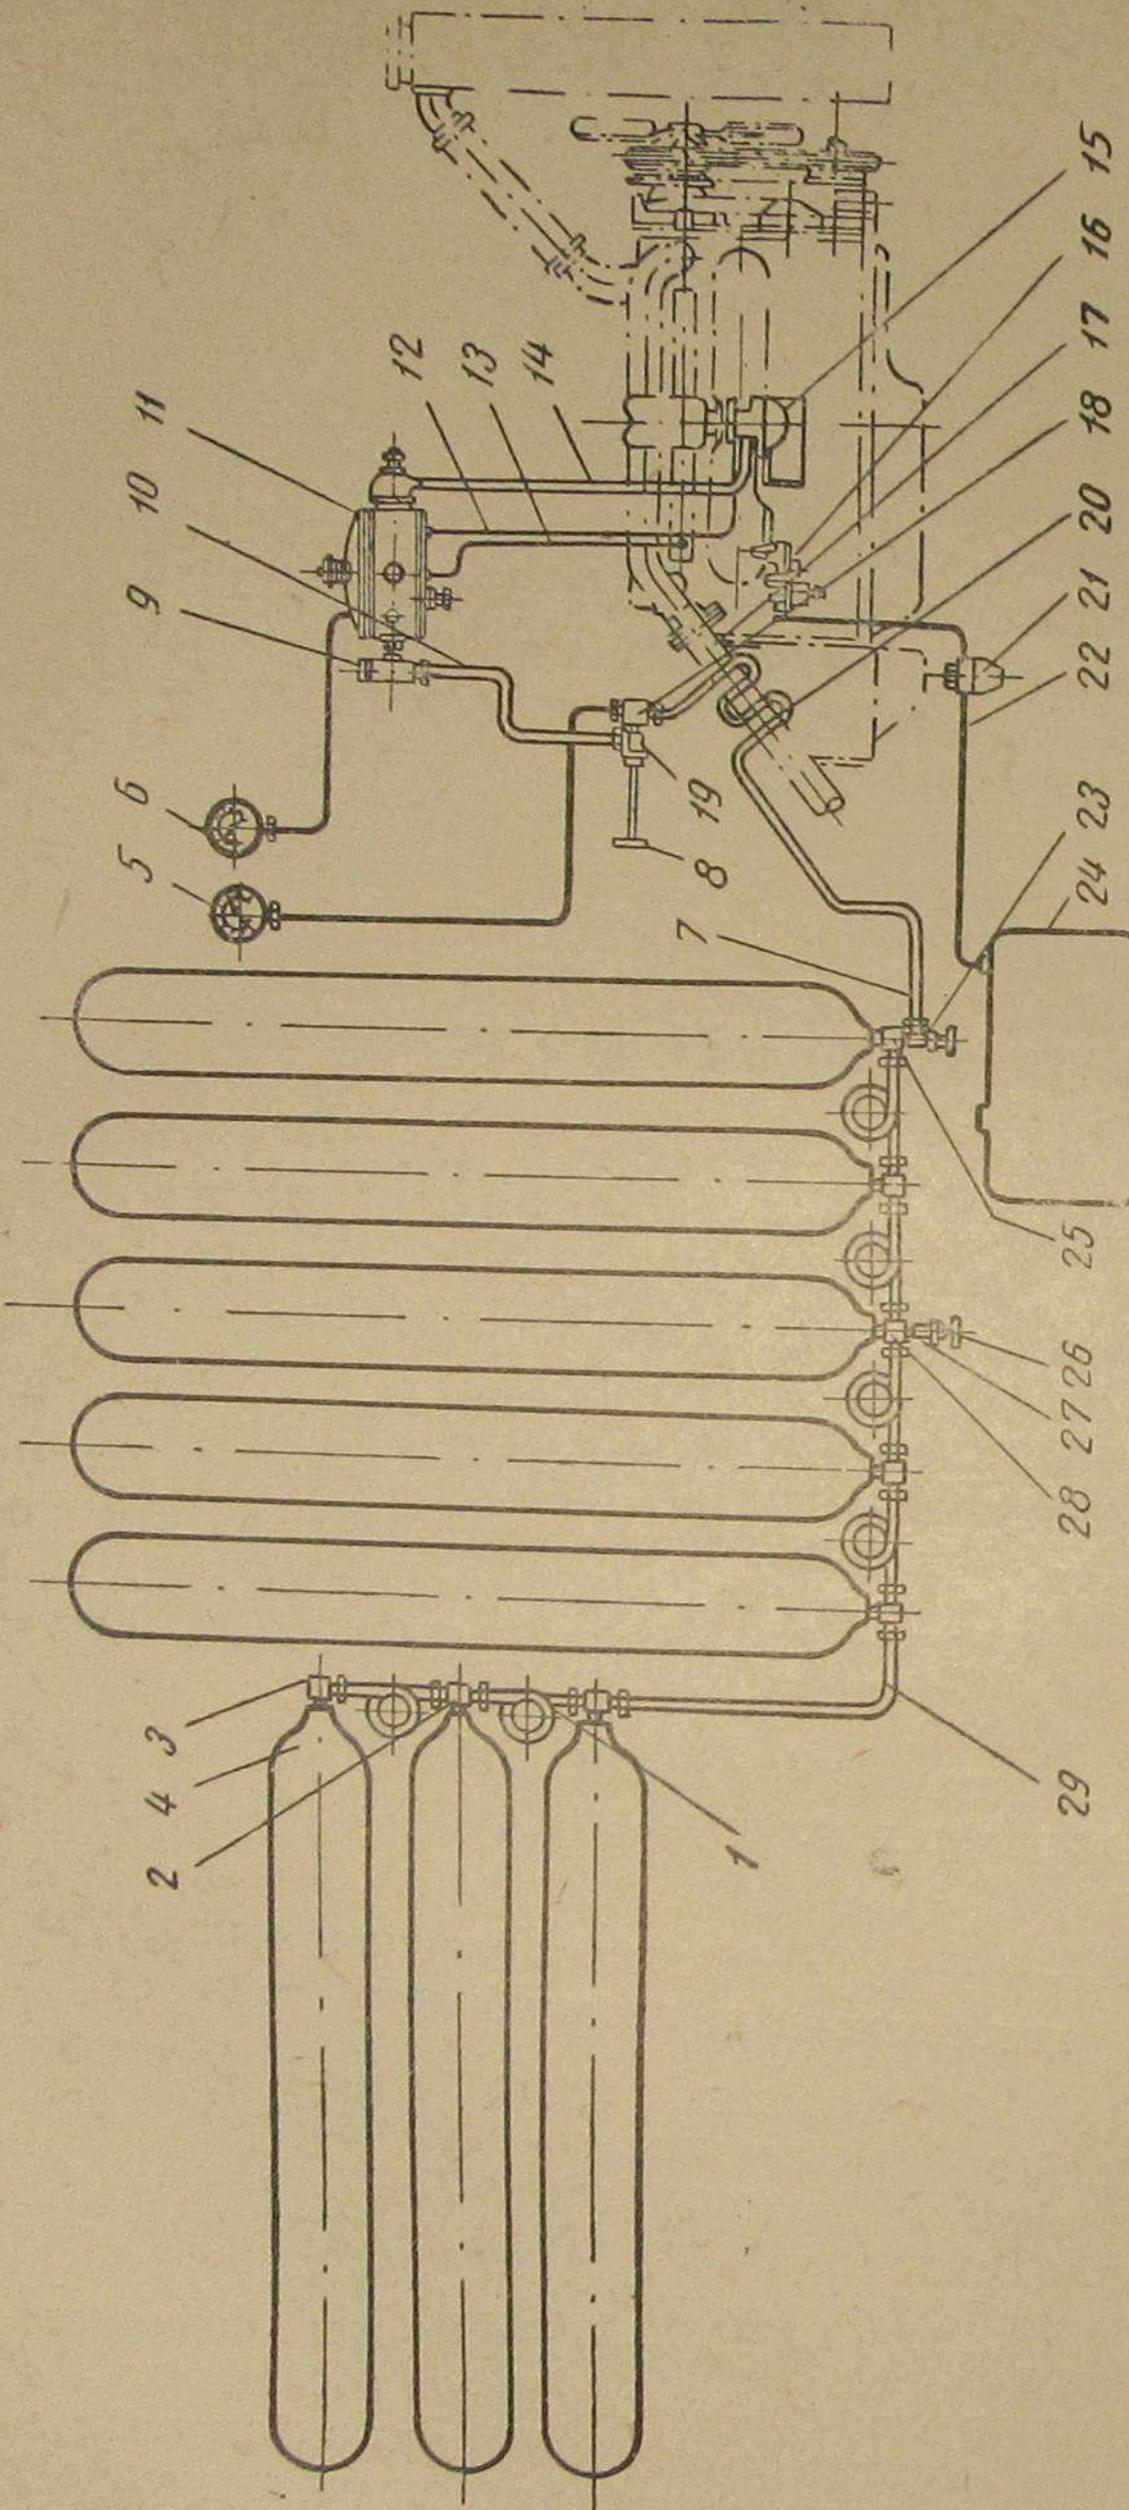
Схема газового оборудования автомобиля ЗИС-156:
